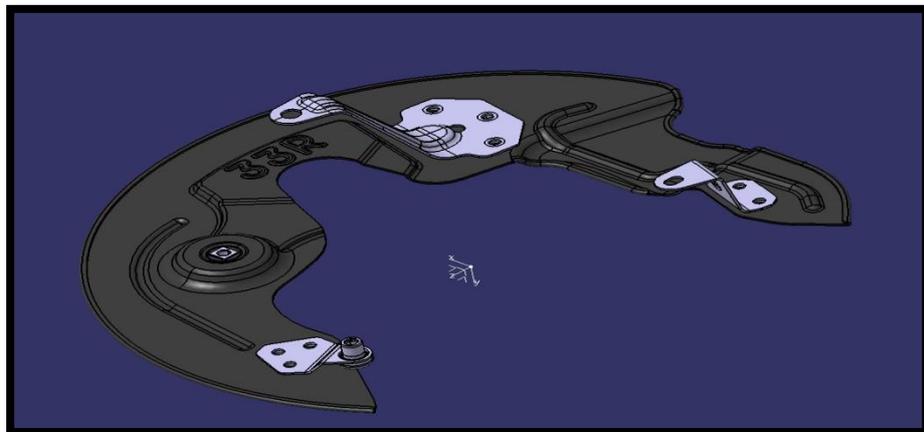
version finale d'assemblage protecteur et pattes de fixation
